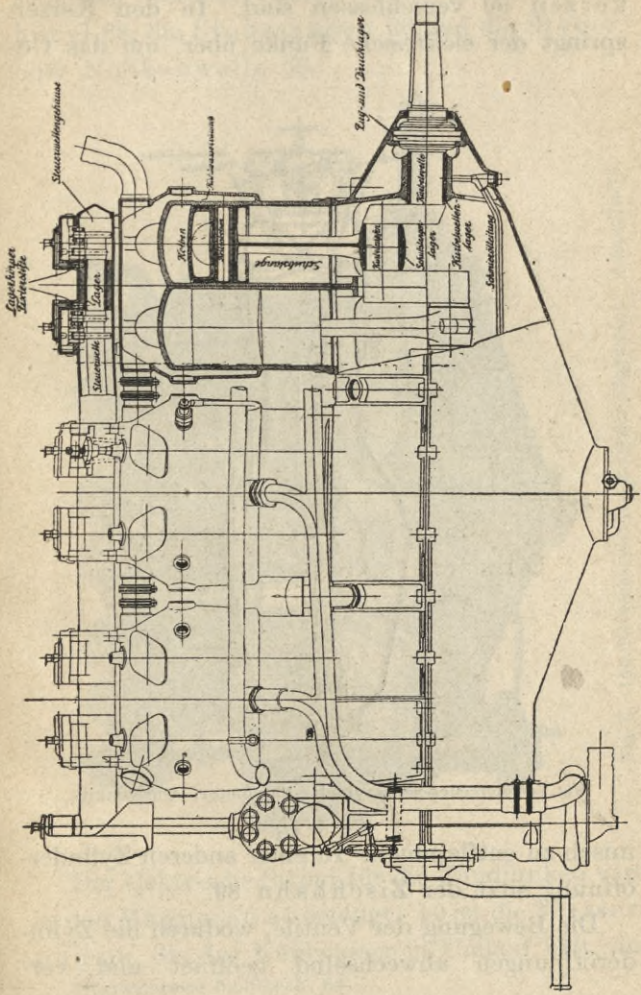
Mercedes-Sechszylinder-Flugmotor. Längsschnitt.
